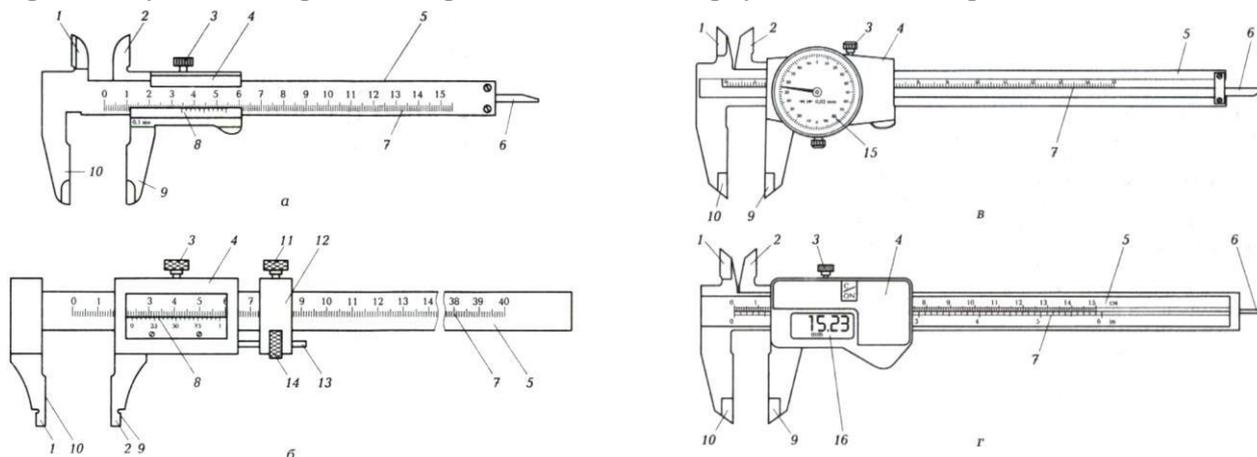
Штангенциркули ШЦ-I (а), ШЦ-III (б), ШЦК-1 (в), ШЦЦ-1 (г): 1, 2 — губки для внутренних измерений; 3, 11 — винты; 4 — рамка; 5 — штанга; 6 — глубиномер; 7 — шкала штанги; 8 — нониус; 9, 10 — губки для наружных измерений; 12 — устройство для тонкой установки рамки; 13 — винт микрометрической подачи; 14 — гайка; 15 — круговая шкала; 16 — панель цифровой индикации
